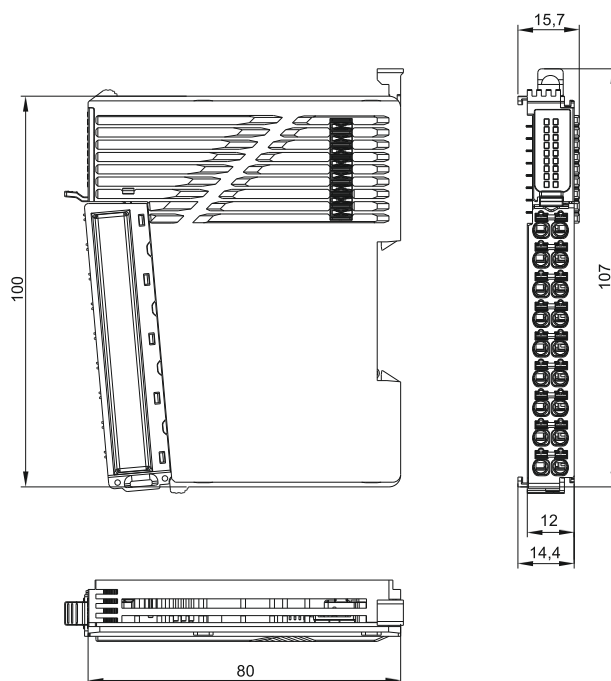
Габаритные и установочные размеры модуля ввода-вывода
